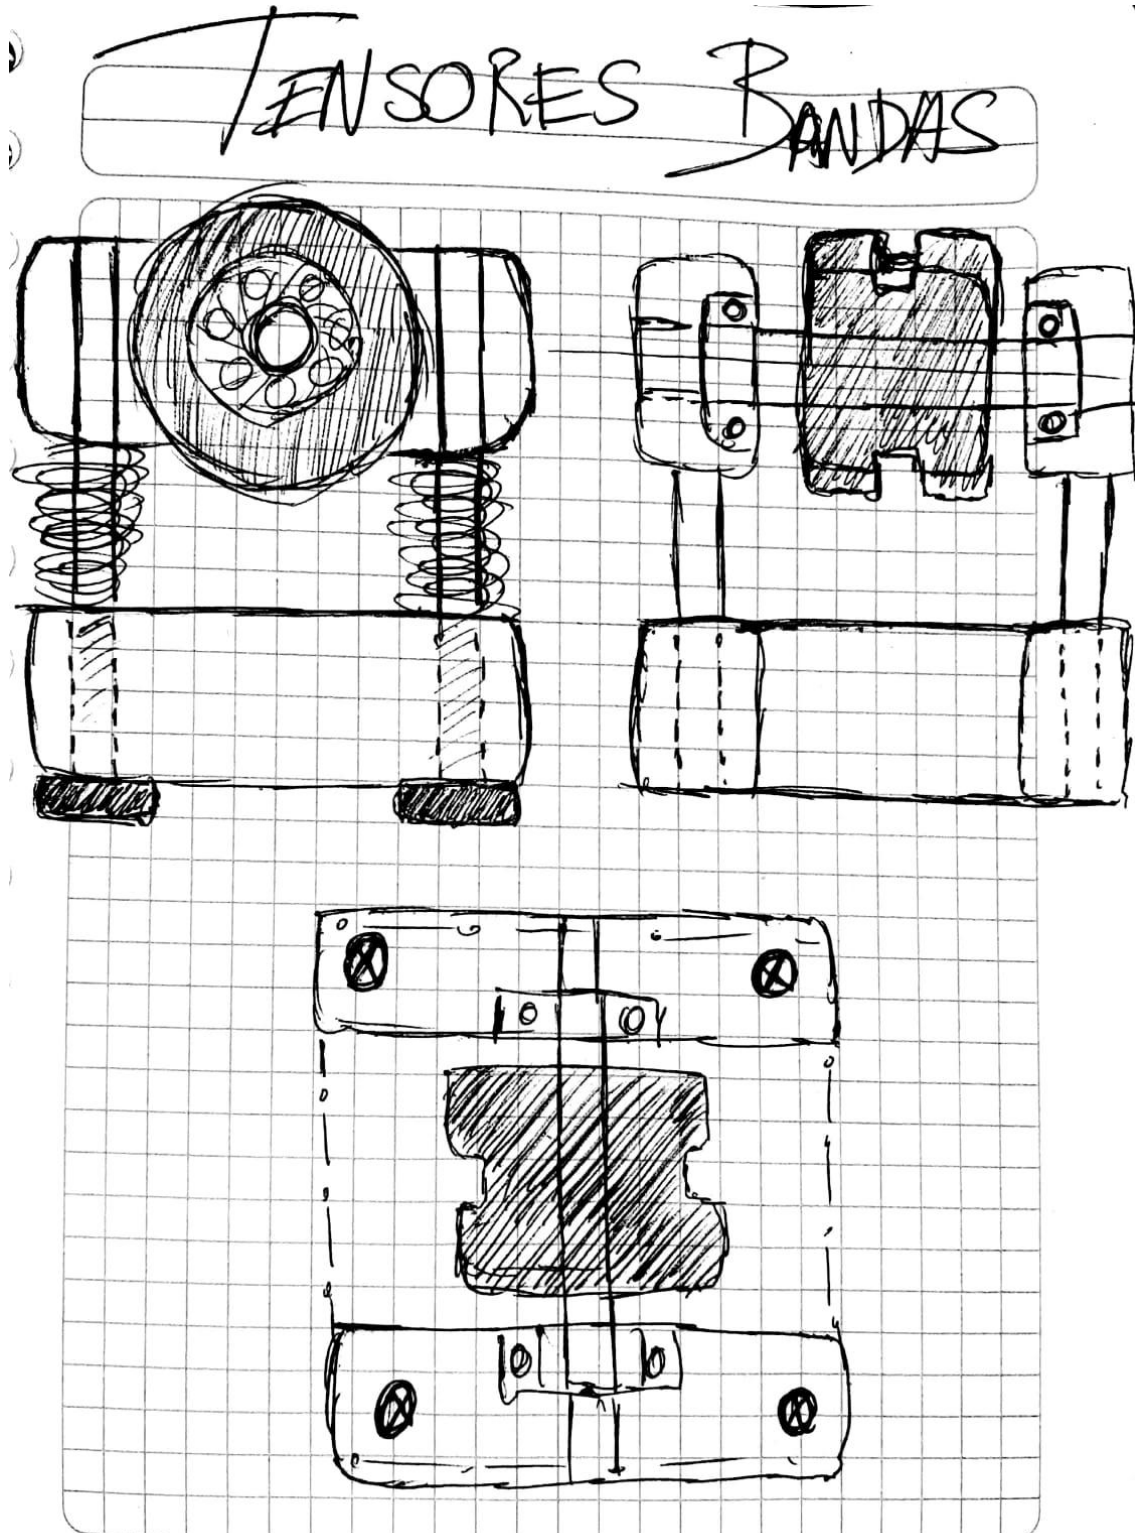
Sketch de detalle de la propuesta para el sistema de tensión.
